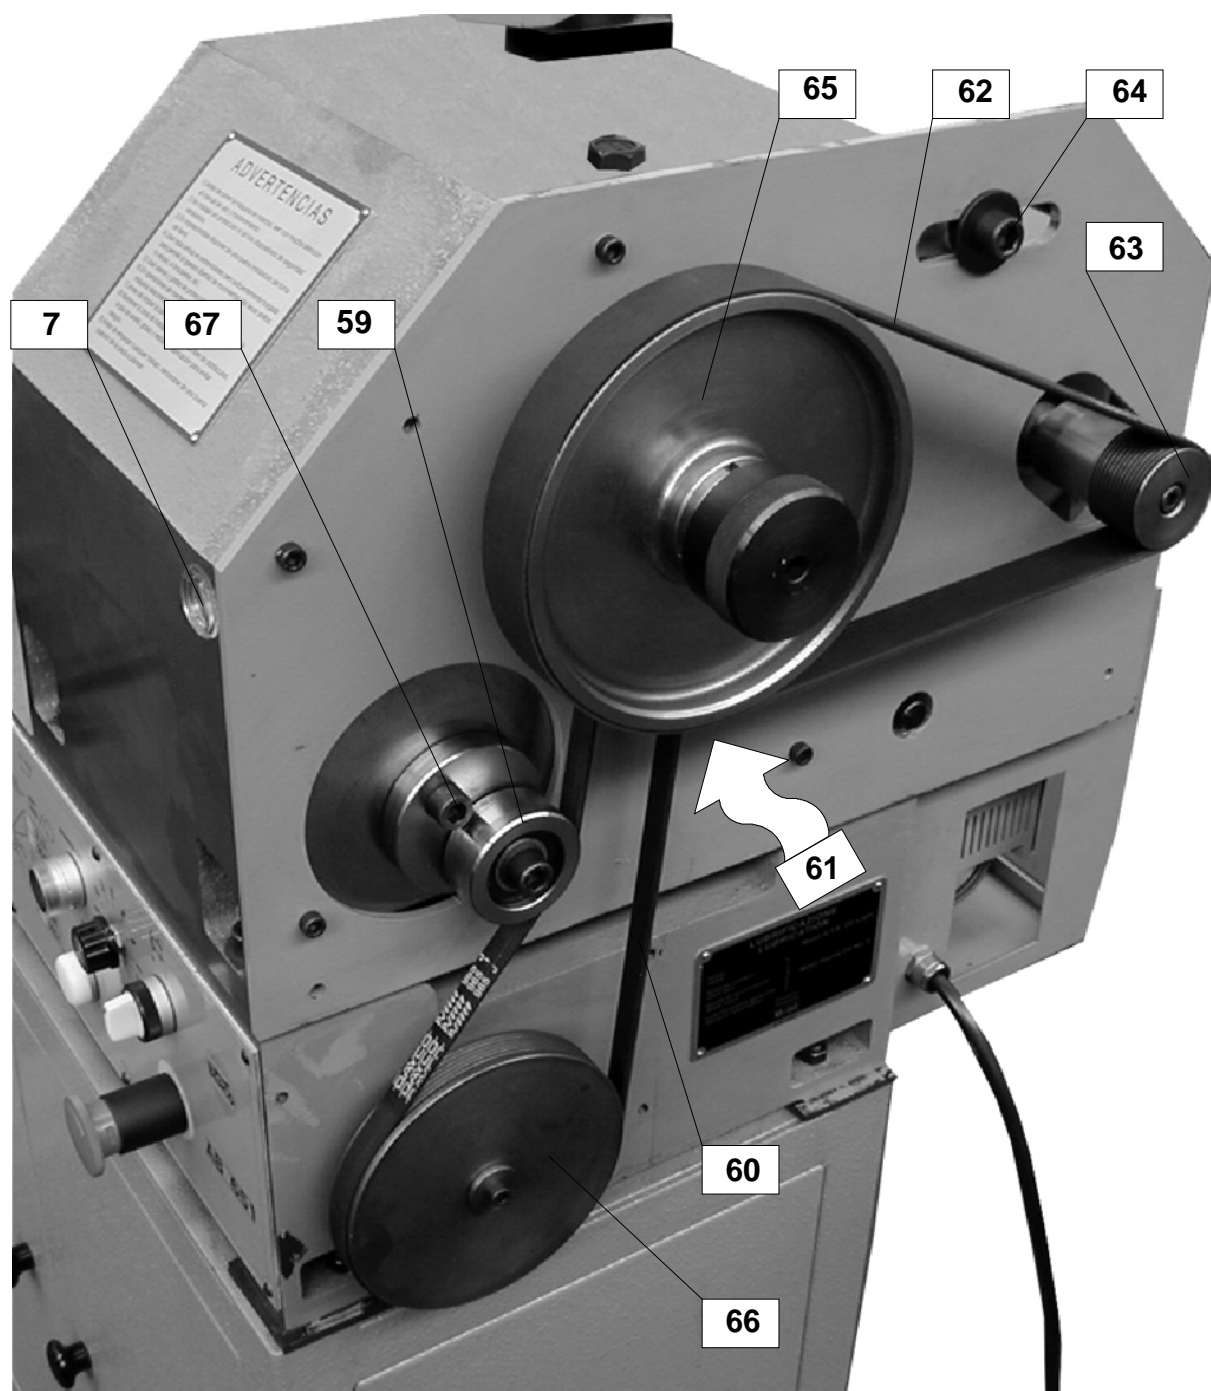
ВИД СТАНКА СБОКУ С ОТКРЫТЫМ ЗАГРАЖДЕНИЕМ
